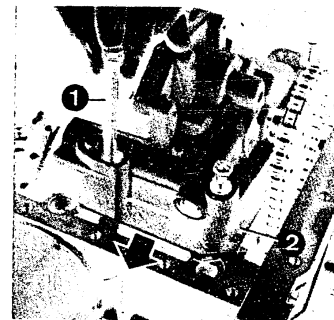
Bei der Demontage der Ölpumpe sind die Befestigungsschrauben (1) zu entfernen und die Zwischenscheibe (2) in Pfeilrichtung herauszuziehen.
